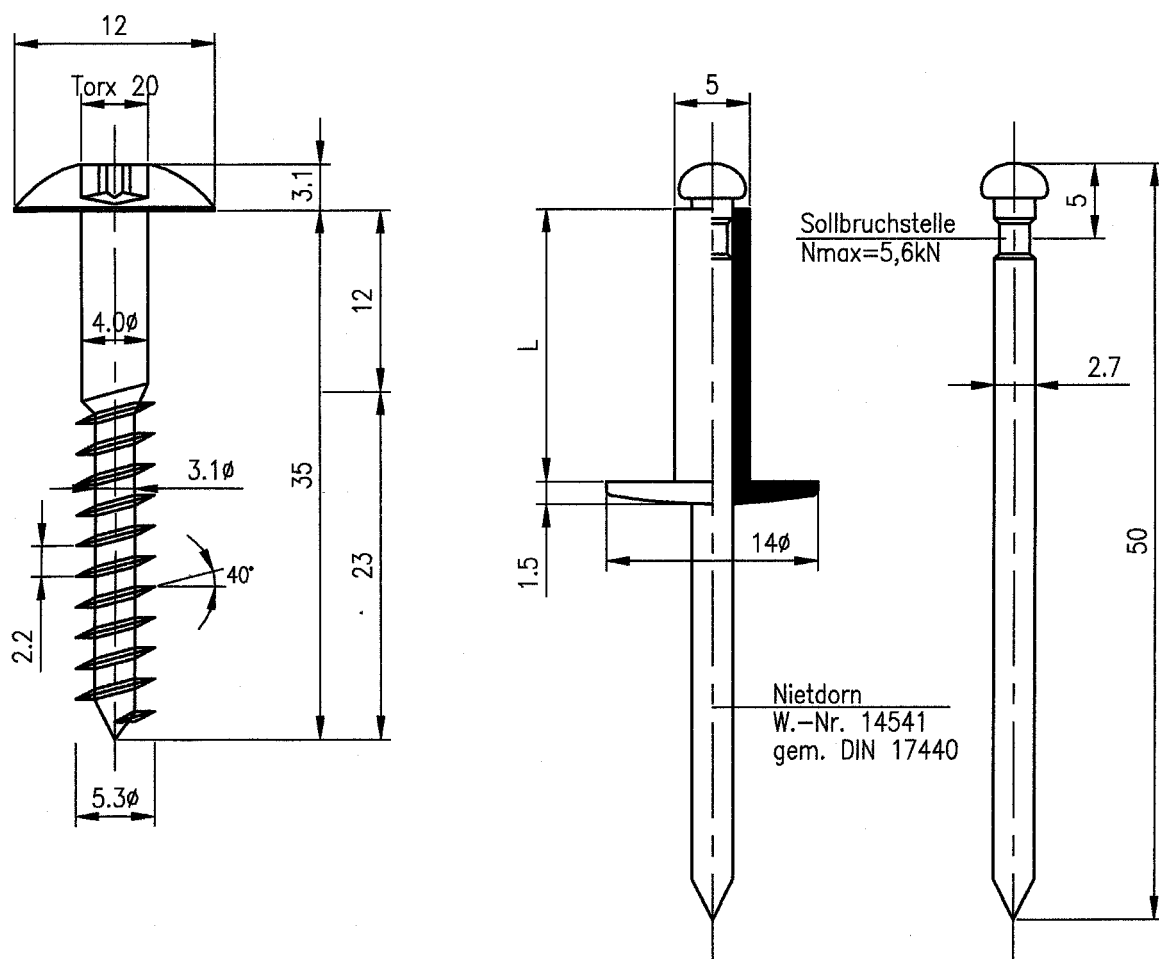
panneaux de facade MAX EXTERIOR – matériel de fixation
